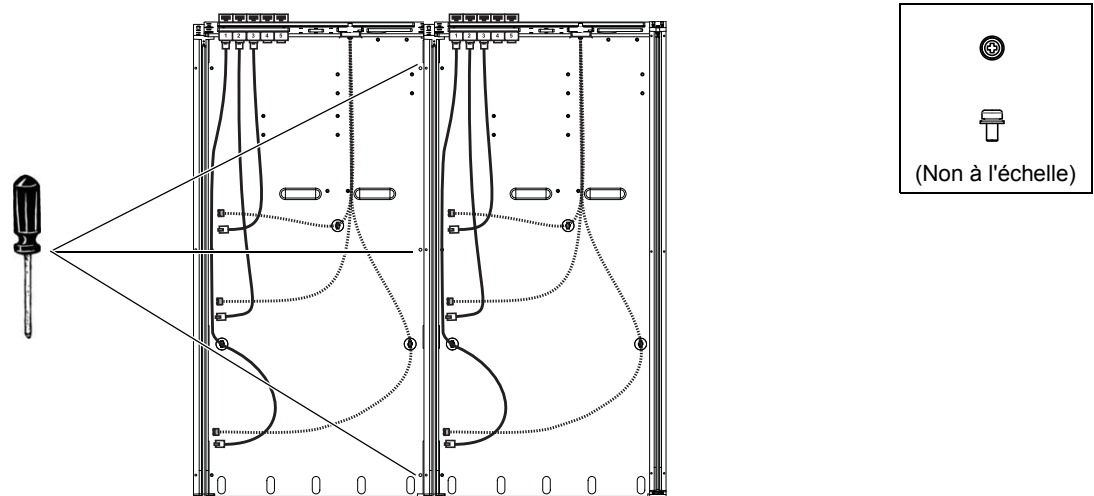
Fixation de la plaque de fond du premier bac à la paroi latérale du second bac
